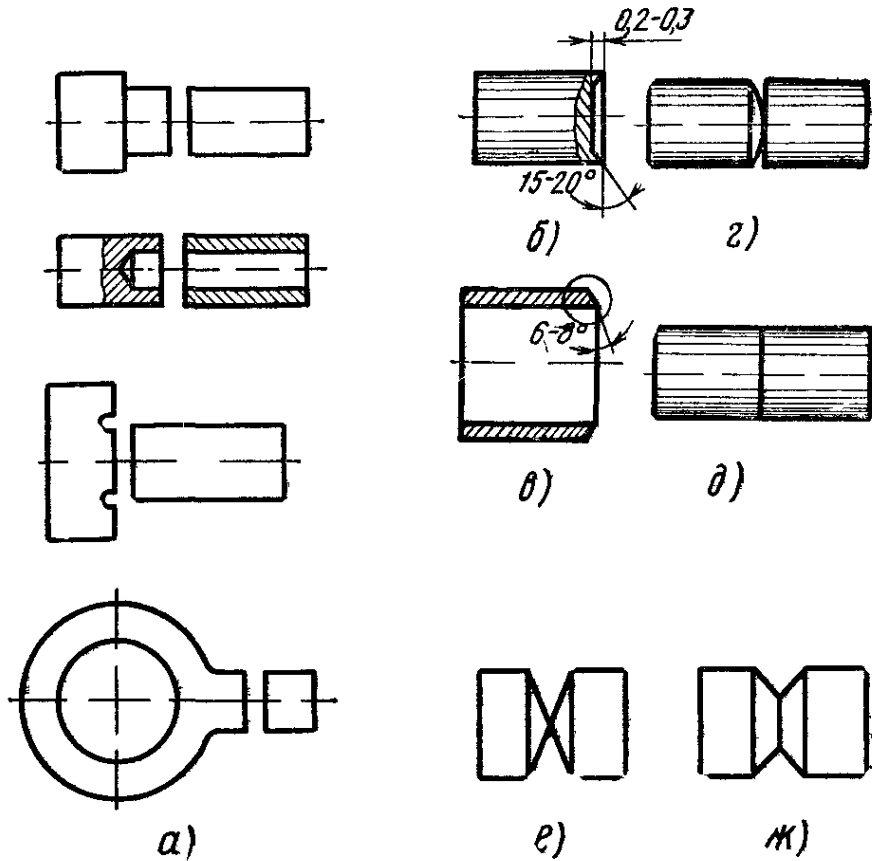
Подготовка деталей к сварке оплавлением (а) и сопротивлением (б — ж)
